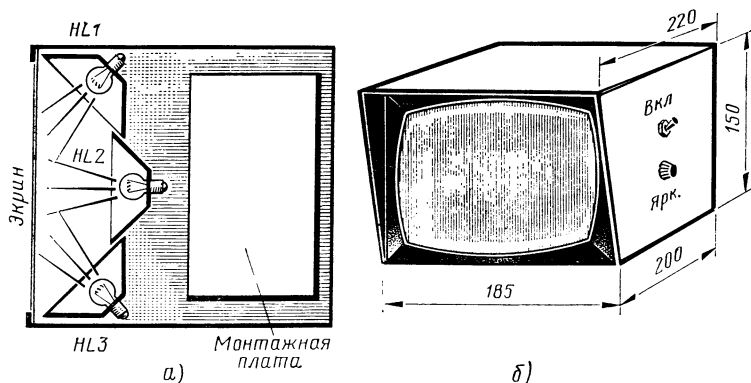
Расположение ламп внутри корпуса (а) и внешний вид (б) приставки
